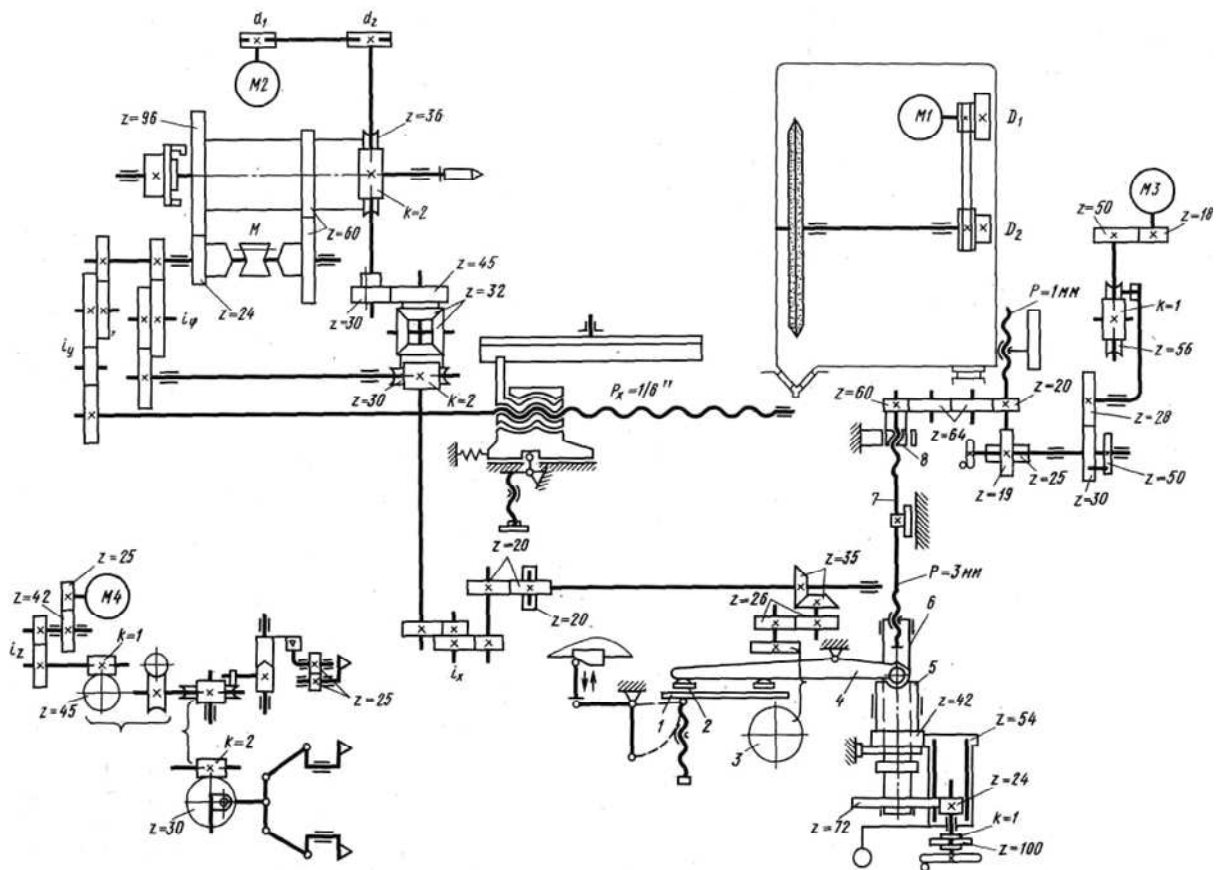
Кинематическая схема универсального резьбошлифовального станка
